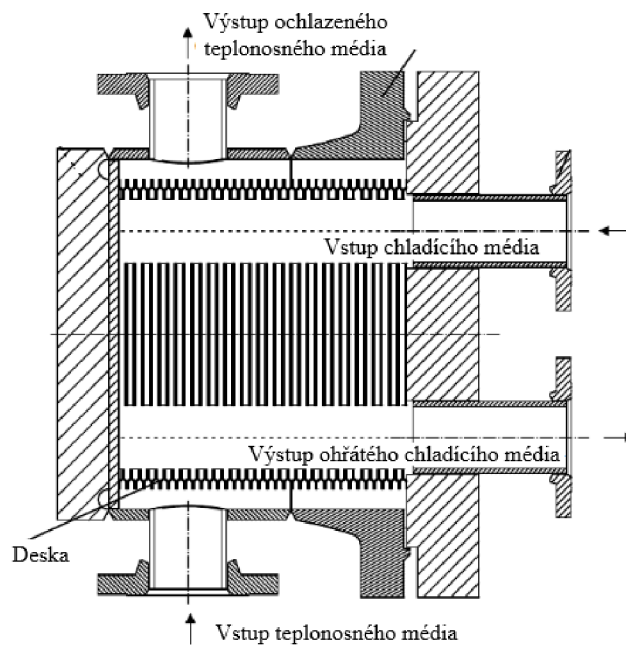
Schematické zobrazení proudů v deskovém výměníku [22] (upraveno).
